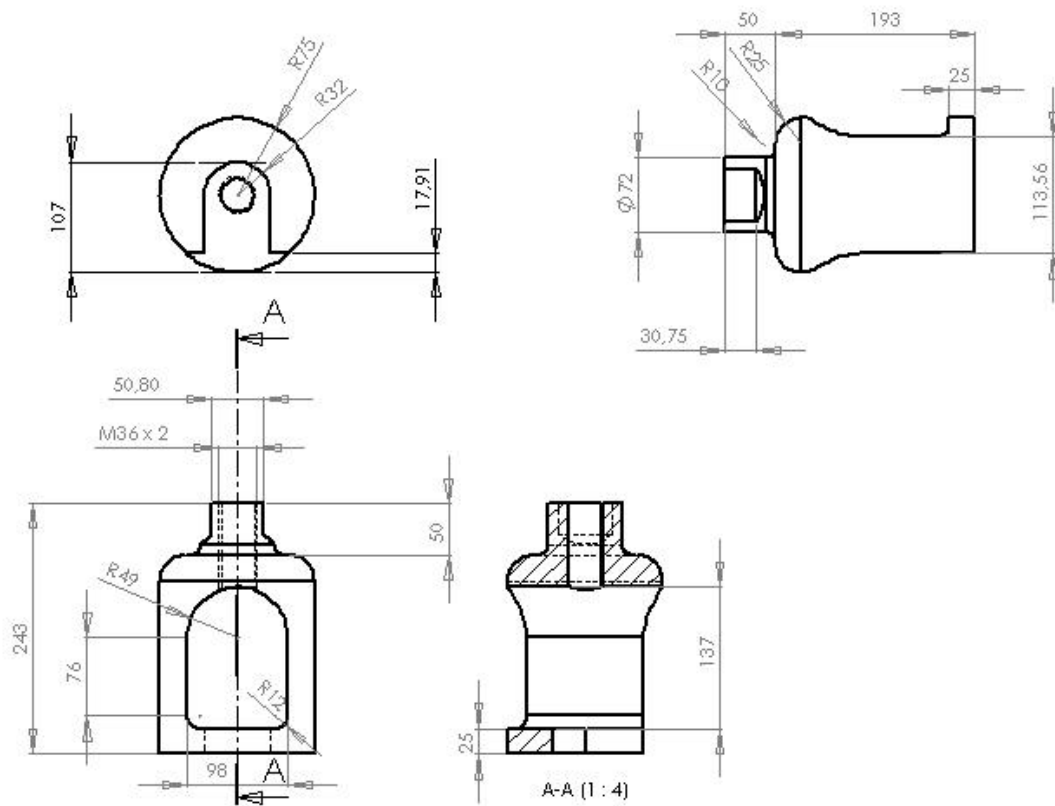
Dimensões do dispositivo suporte para ensaio de fadiga.
